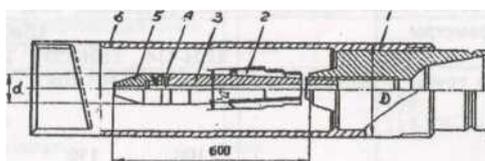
Труболовка внутренняя универсальная для утяжеленных буровых труб (ТВУ-УБТ): 1-переводник; 2-ловильная втулка; 3-корпус; 4-уплотнительный элемент; 5-наконечник; 6-направление
